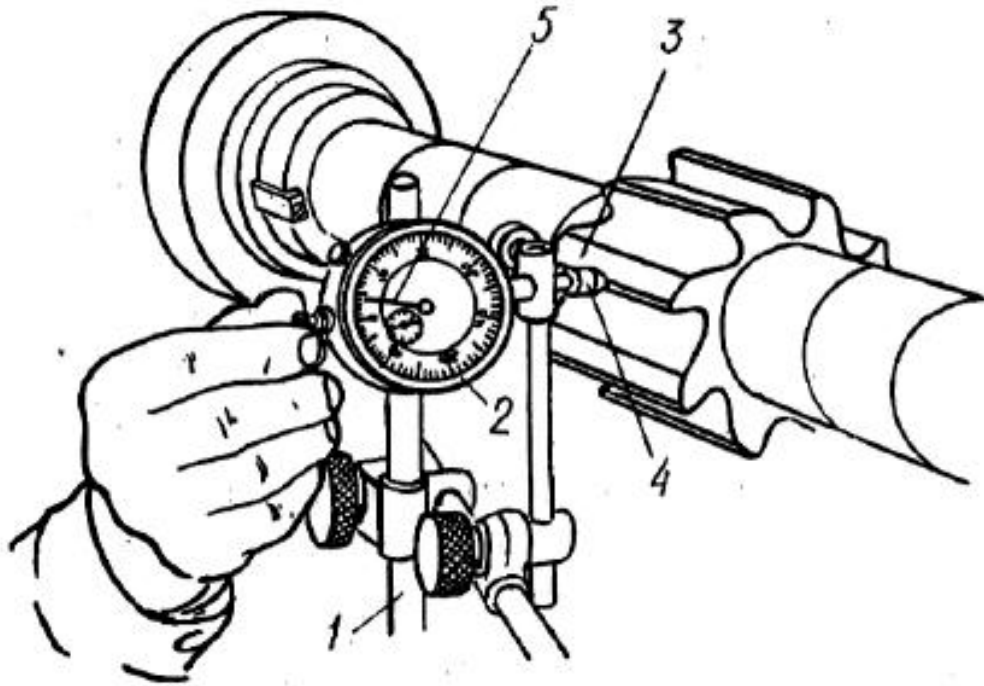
Установка фрезы 1 - штатив; 2 - индикатор; 3 - зуб фрезы; 4 - голка; 5 - стрелка
